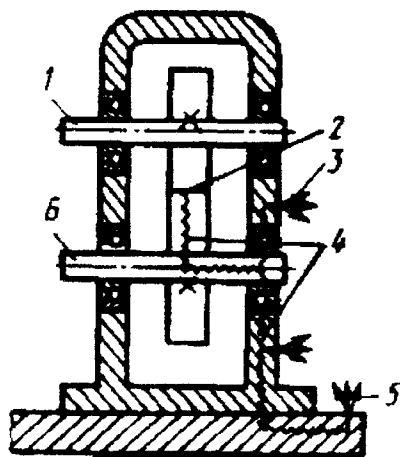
Схема передачи звука в зубчатом приводе:
